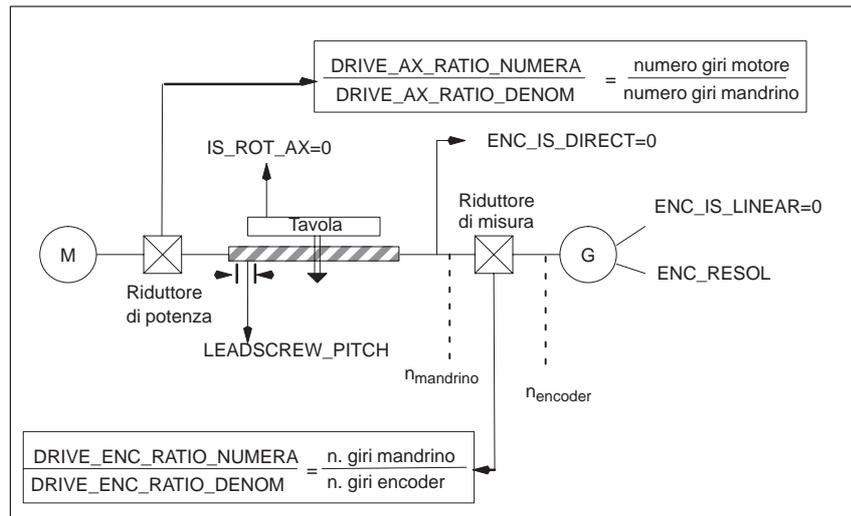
Asse lineare con encoder rotativo sulla macchina
